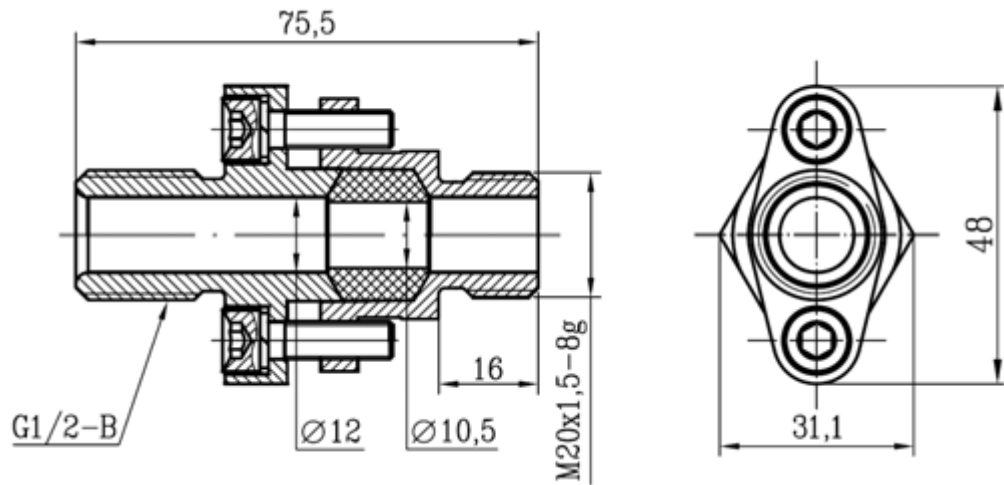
Ввод кабельный для трубного монтажа (ТБ 1/2")
